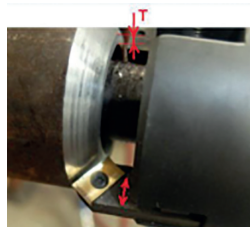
Точная установка держателей резцов обеспечивает постоянное притупление
